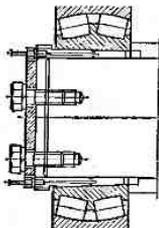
Гидравлический монтаж с использованием каналов во стальной втулке
